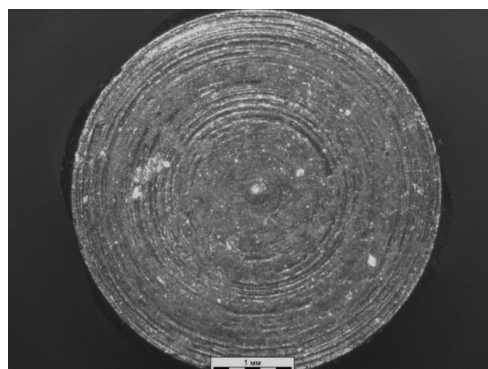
Рабочая поверхность посадочного штока капсюлятора
